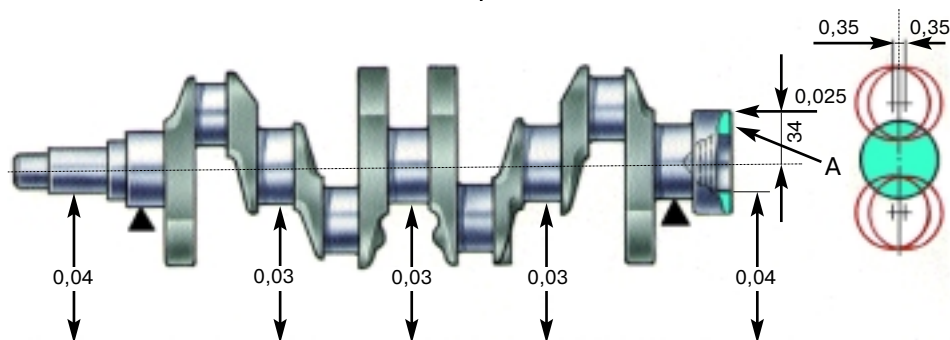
Допустимые биения основных поверхностей коленчатого вала двигателя мод. 2106-70
